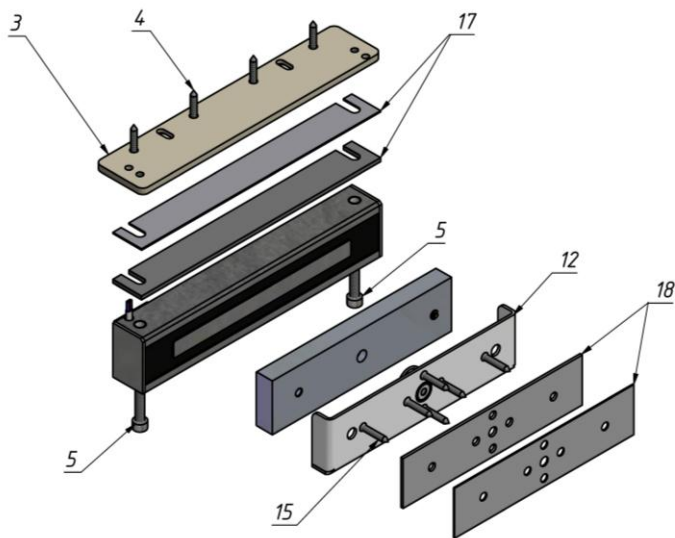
Регулировка положения корпуса и якоря с помощью пластин
